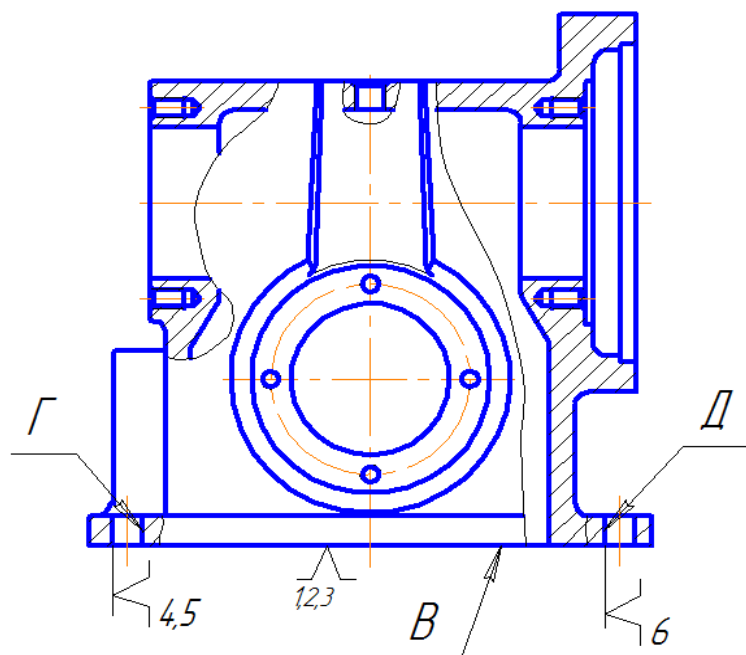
Чистовые базы предлагаемого тех. процесса
